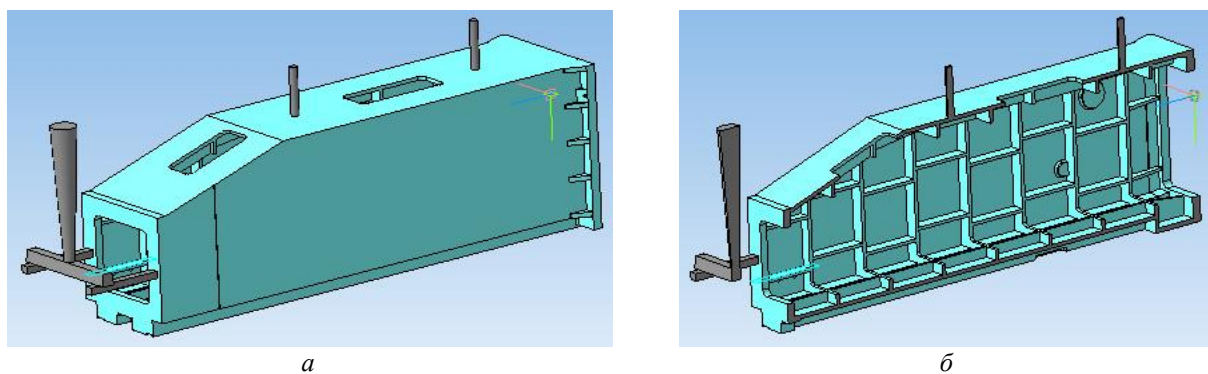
Трехмерная модель отливки с литниково-питающей системой (а) и разрез модели отливки (б)
